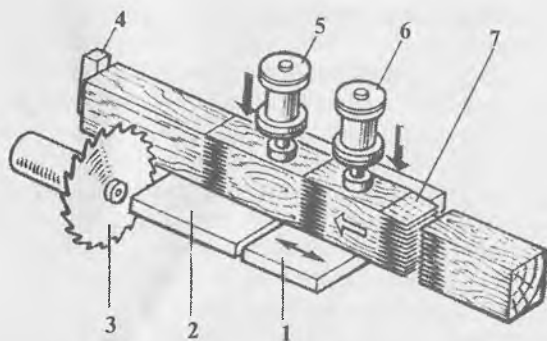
Схема пресса для склеивания прямолинейных заготовок на зубчатый шип:
